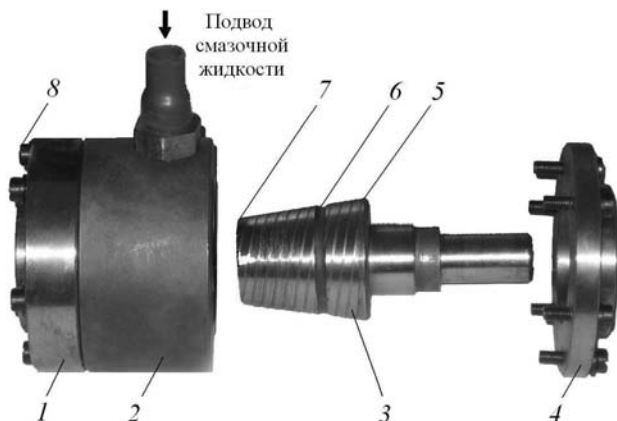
Опытный образец подпятника с винтовой нарезкой конусной пяты: 1 — подпятник; 2 — корпус; 3 — пята; 4 — крышка корпуса; 5 — многозаходная винтовая нарезка; 6 — ров подвода смазочной жидкости; 7 — фаска; 8 — крепежные болты
